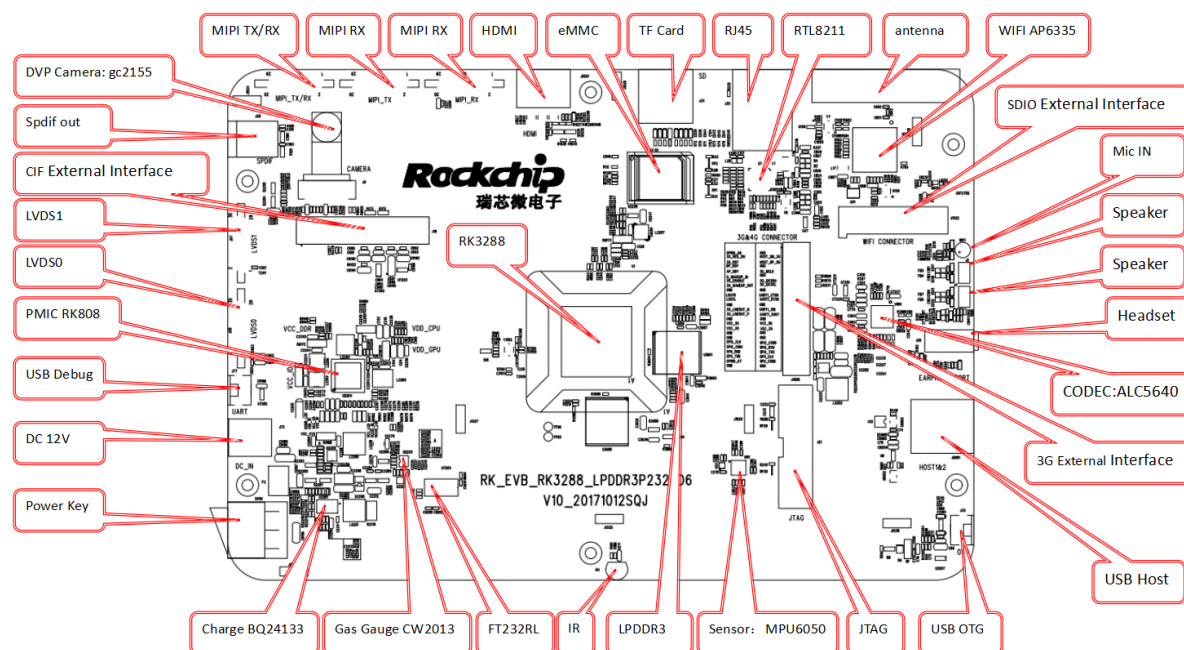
RK3288 EVB 2.0 PCB 上 TOP Layer 模块布局位置图
